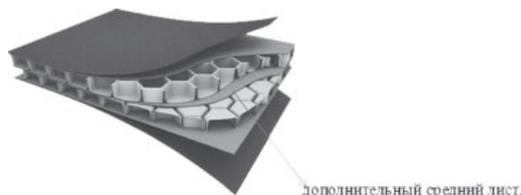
Конструкция BUBBLE GUARD® BOARD Duplex, выпускаемая фирмой Colines.
